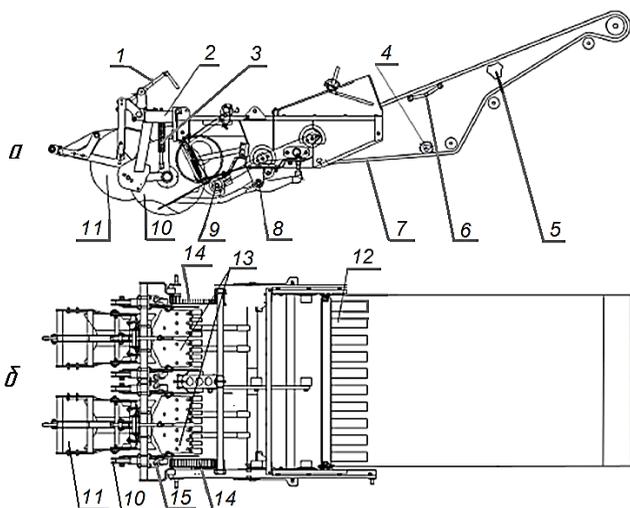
Блок подкапывающе-сепарирующий и первый сепарирующий транспортер: *a* – вид сбоку, *б* – вид сверху; 1 – механизм установки глубины подкапывания пласта; 2 – рама; 3 – механизм установки глубины хода подрезающих дисков; 4 – валец, очищающий транспортер; 5, 6 – встряхиватели пассивные; 7 – элеватор первый сепарирующий; 8 – балка лемехов; 9 – валец ребристый; 10 – диски подрезающие; 11 – катки копирующие; 12 – разравниватель почвы; 13 – лемеха; 14 – колеса ботвозатягивающие; 15 – механизм регулирования усилия прижатия ботвозатягивающих колес к транспортеру
